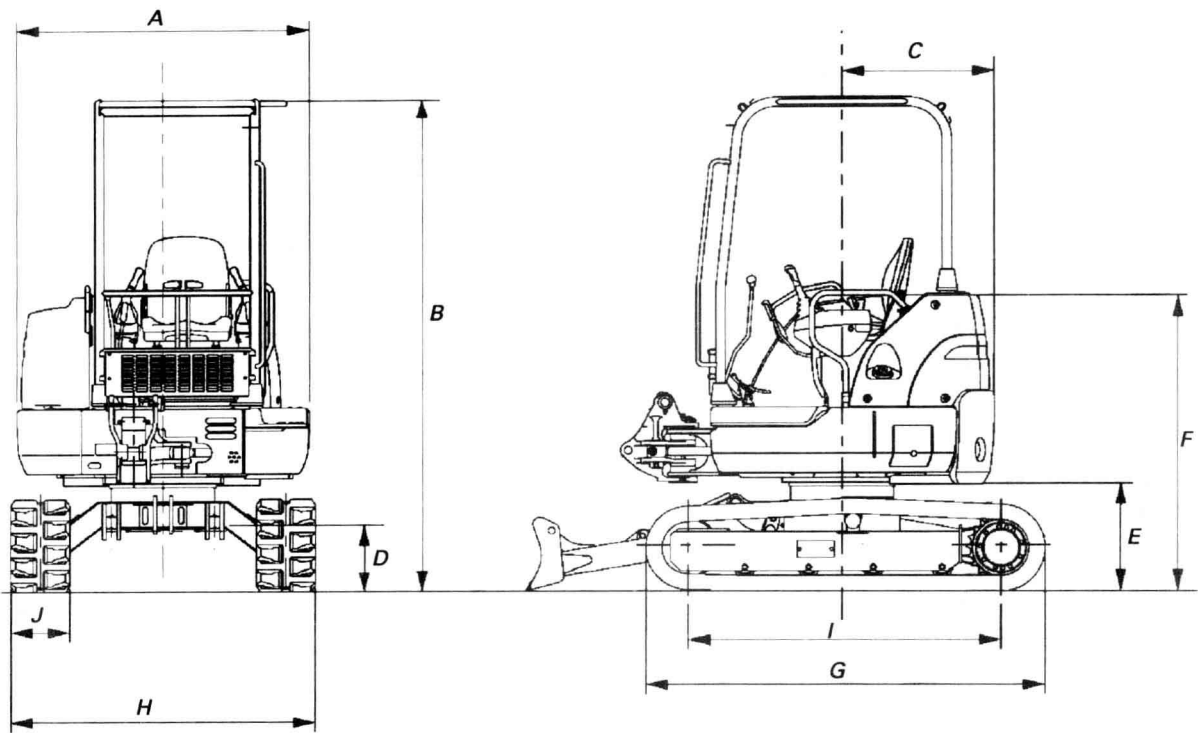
ZAXIS30U 型挖掘机外形尺寸
